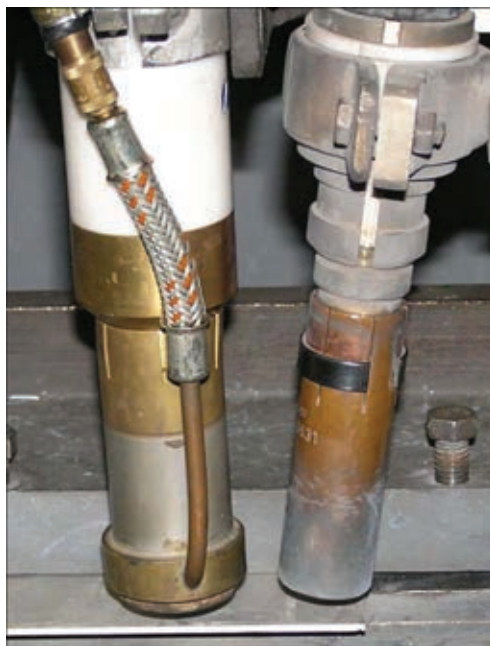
Размещение плазмотрона и горелки плавящегося электрода при комбинированном использовании плазменно-дуговой сварки и дуговой сварки плавящимся электродом
